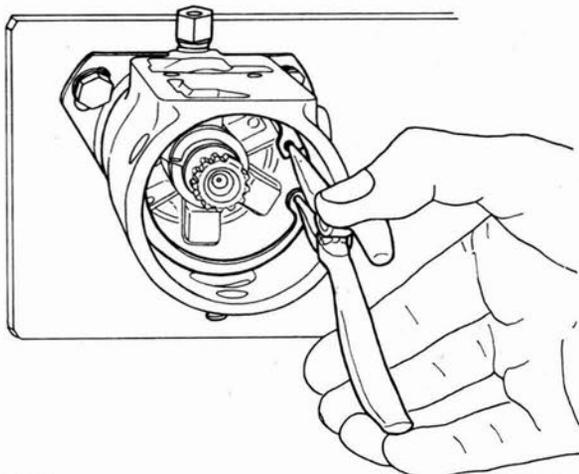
Démontage (remontage) du rotor de la tête hydraulique.
